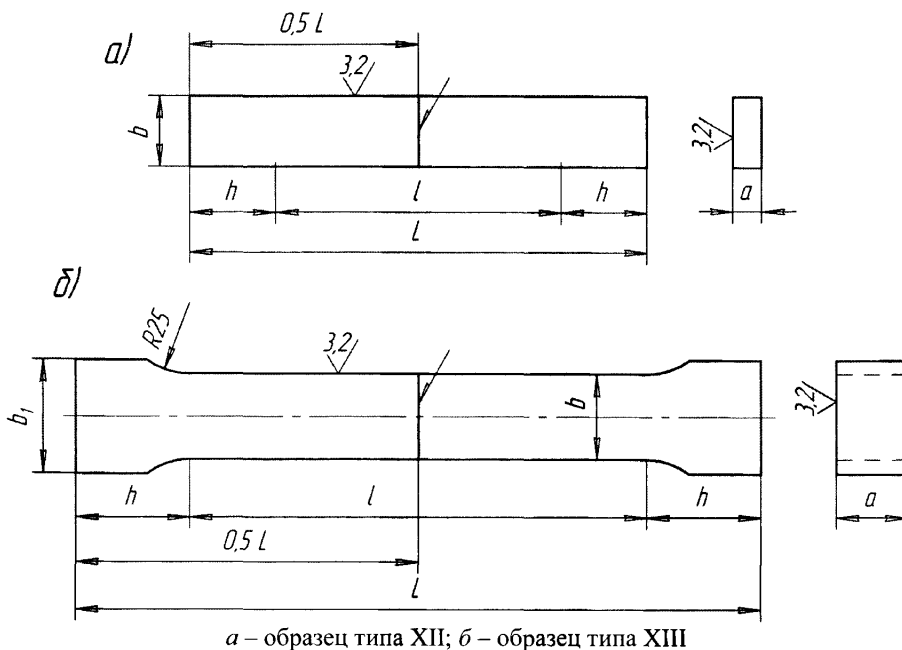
Образцы для определения равнопрочности сварного соединения при растяжении
